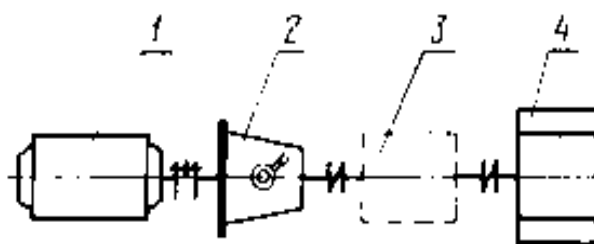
Схема обкатки коробок передач розімкненим методом:
